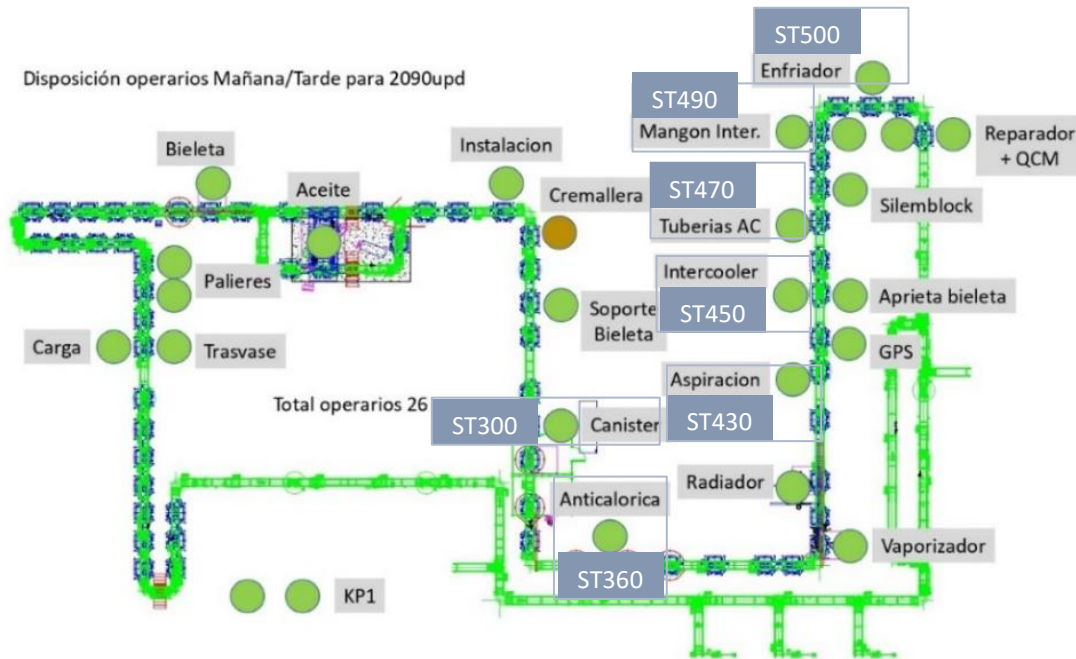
Layout Pallet Conveyor (Fuente: documentos Ford)
